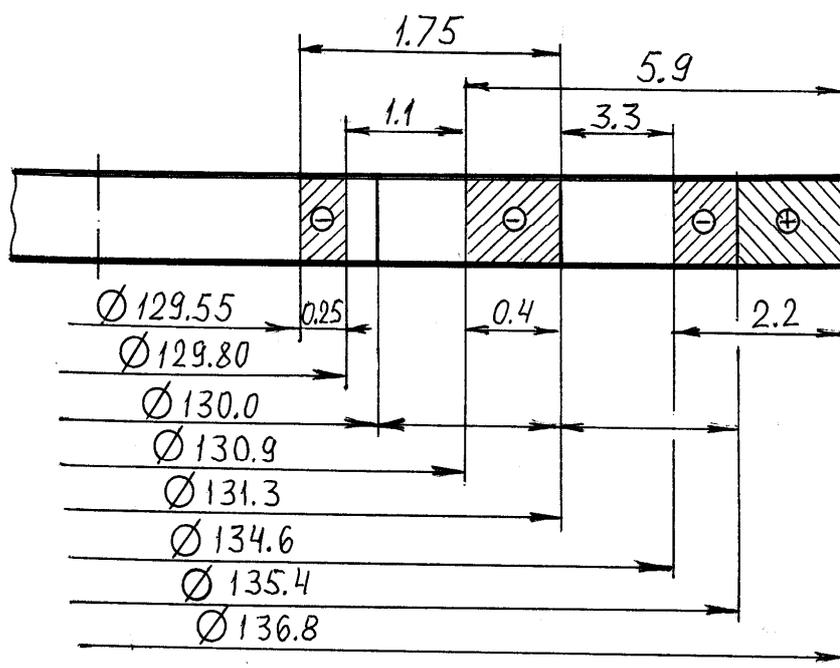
Схема расположения полей припусков и допусков при обработке поверхности Ø130d11
